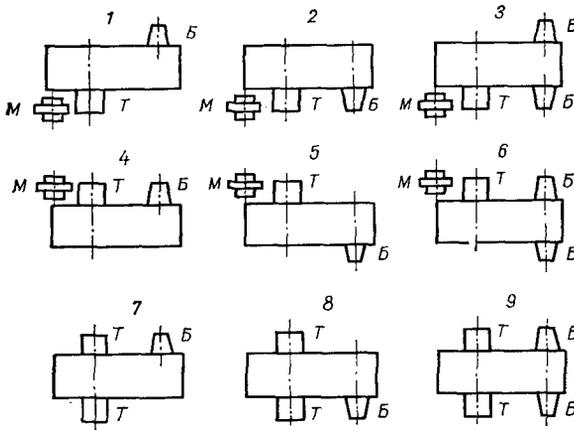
Схемы сборок (1—9) редукторов РЦД:
